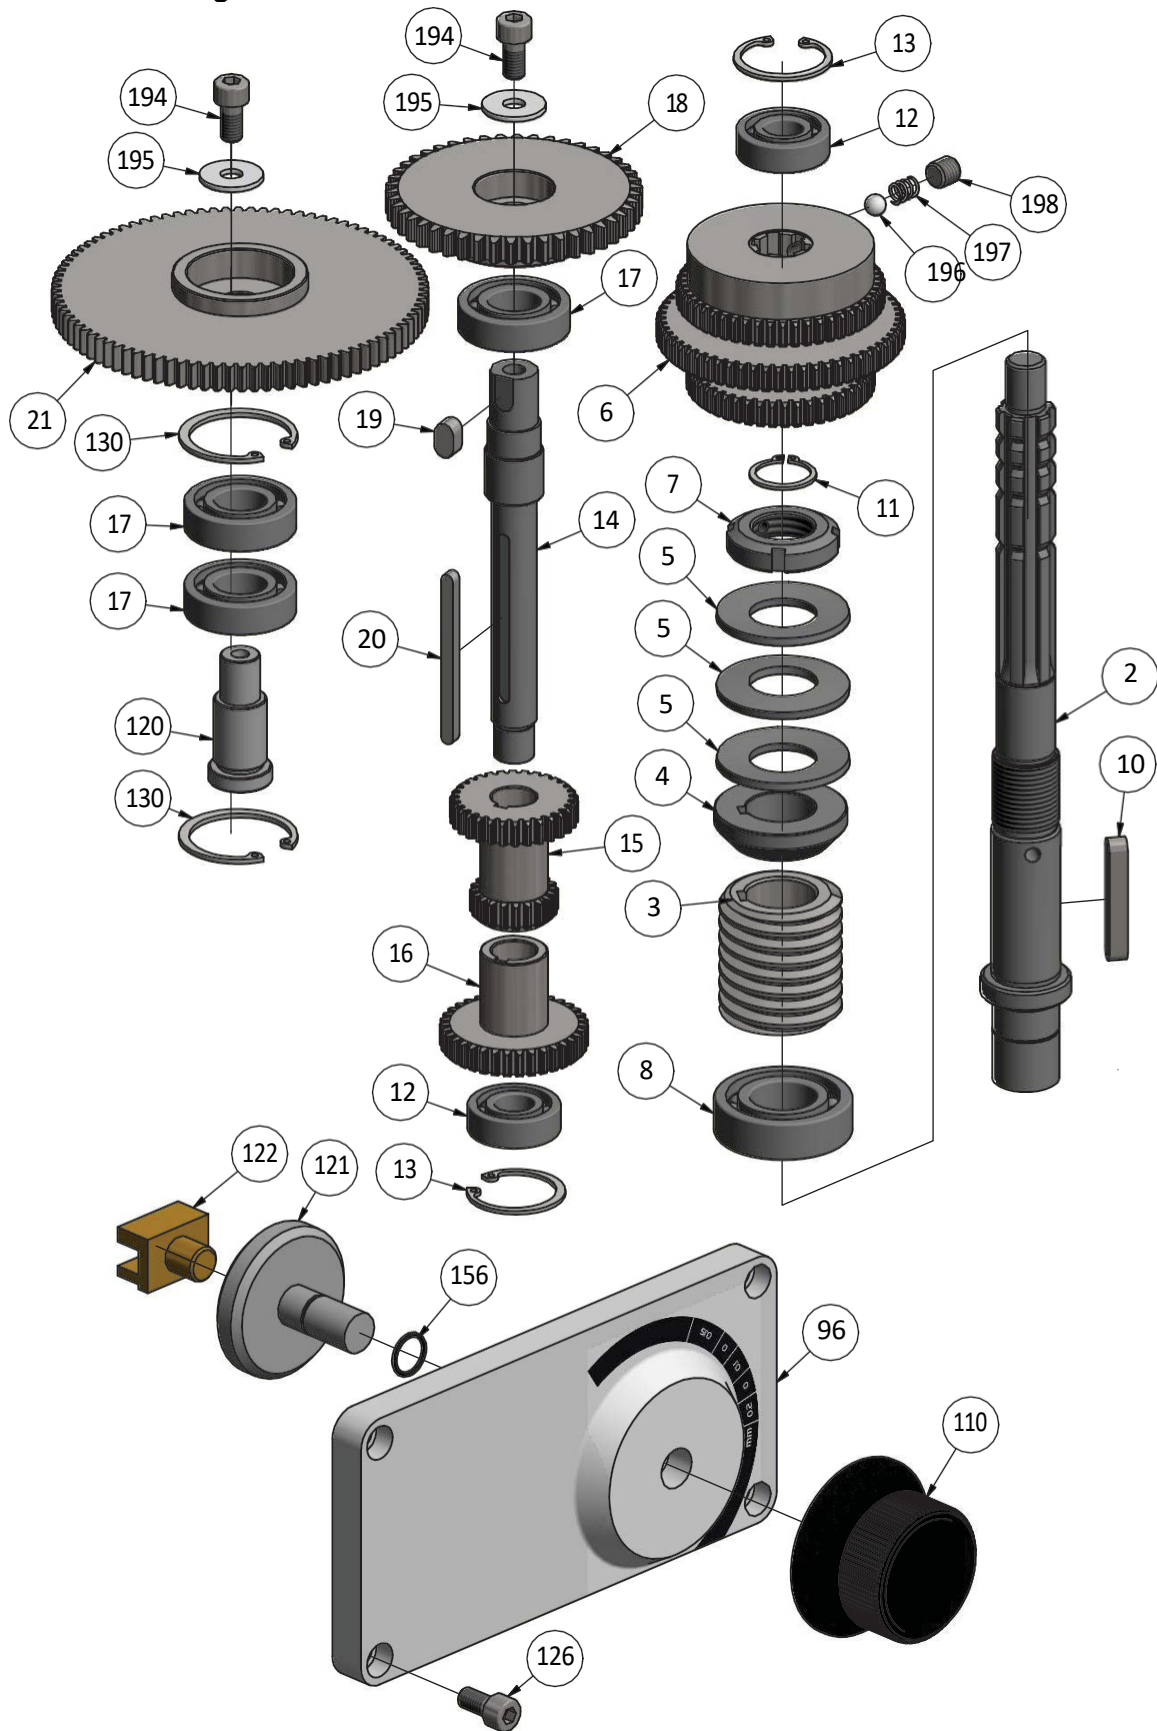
Getriebe Teil B - Tandwielgedeelte B
